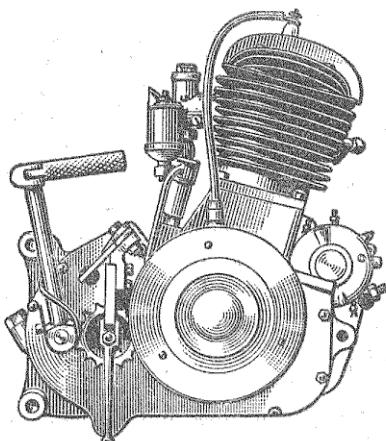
Exemple de moteur incliné (Monet et Goyon).
